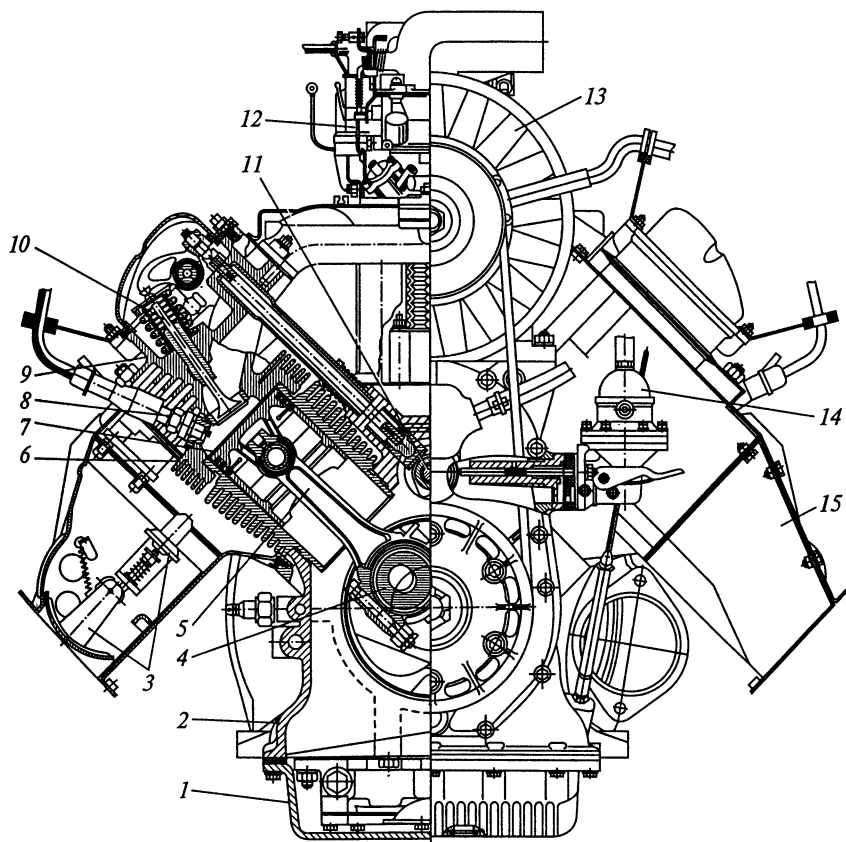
Двигатель легкового автомобиля особо малого класса:
